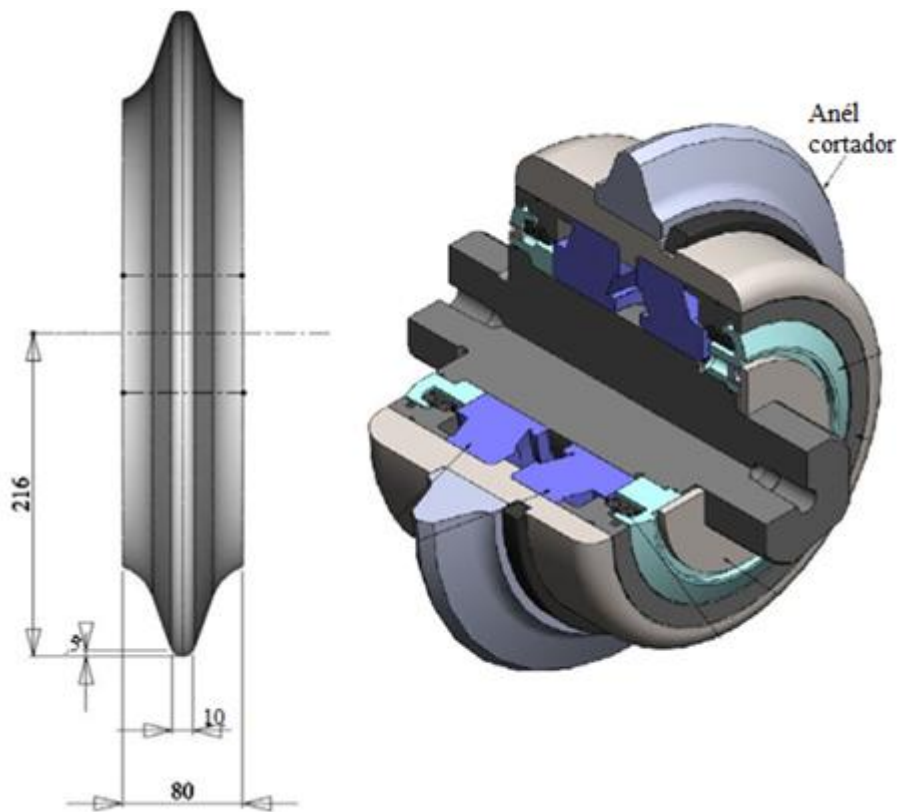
Dimensões (em mm) do disco cortador em corte [23] (Editado)
